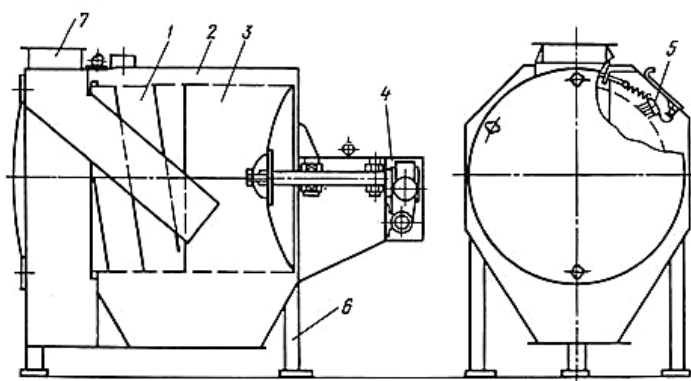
Барабанный скальператор марки А1-БЗО:
